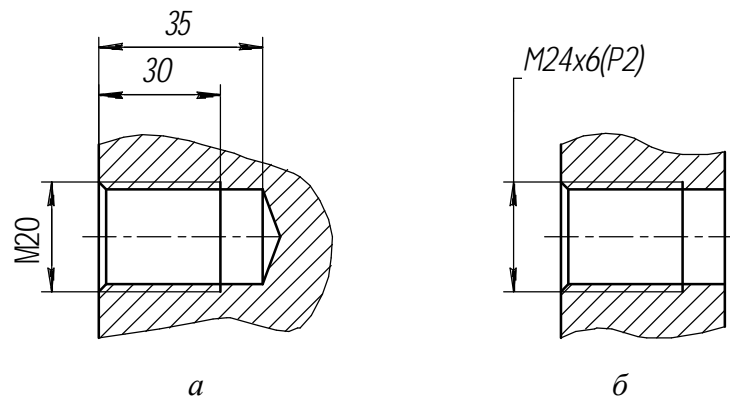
Нанесение размеров метрической резьбы в отверстии
